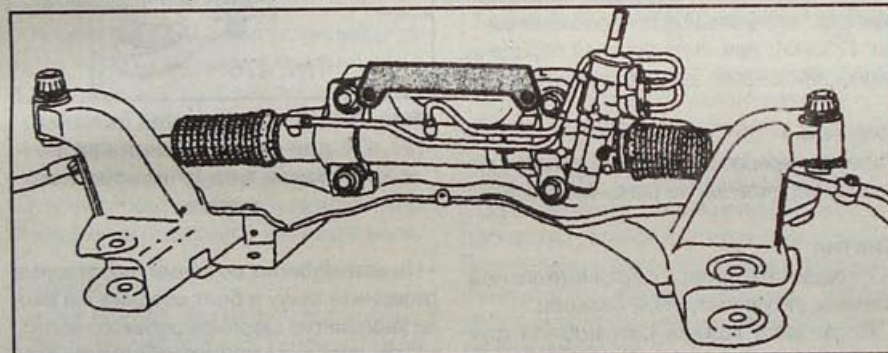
Установка приспособления Dir. 1303-01 для блокировки рулевой передачи на подмоторной раме
